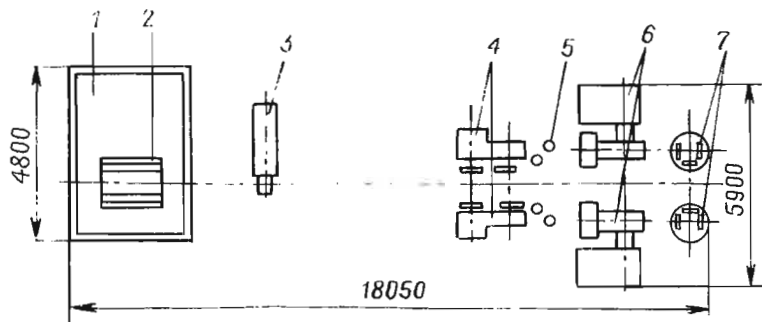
Агрегат для изготовления витого металлокордного брекера:
